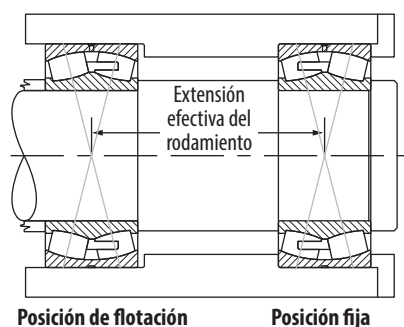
Montaje directo del rodamiento de rodillos esféricos.
